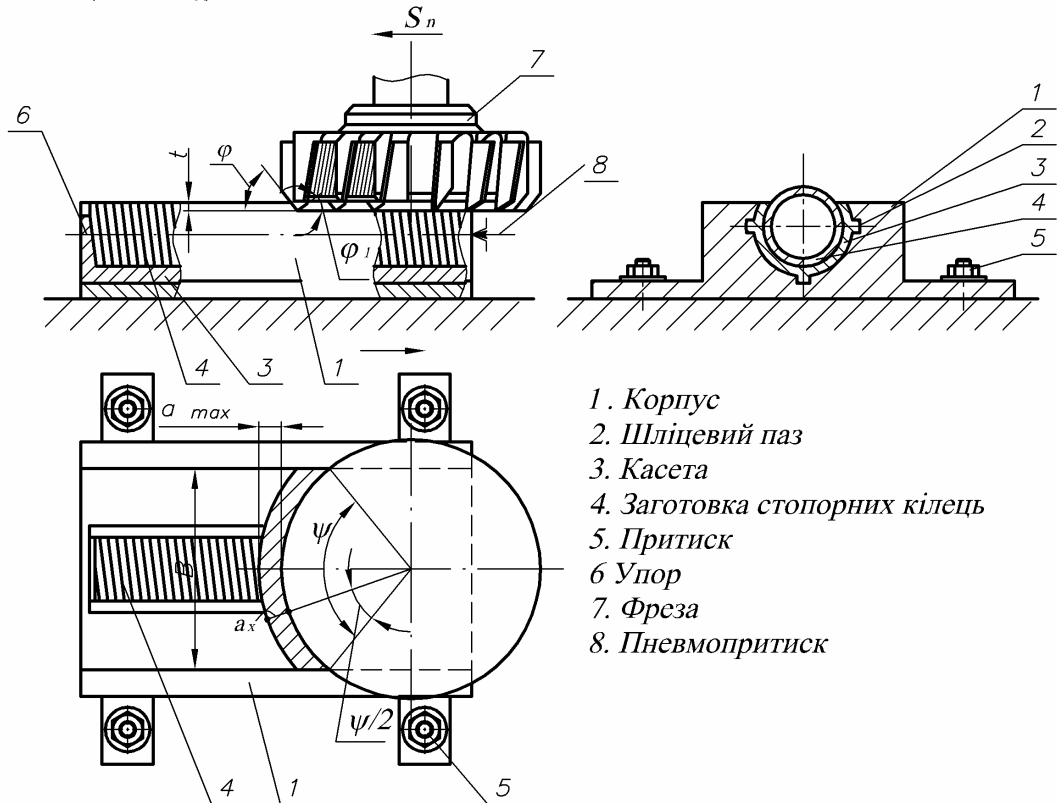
Пристрій для фрезерування і розрізання заготовок стопорних кілець
